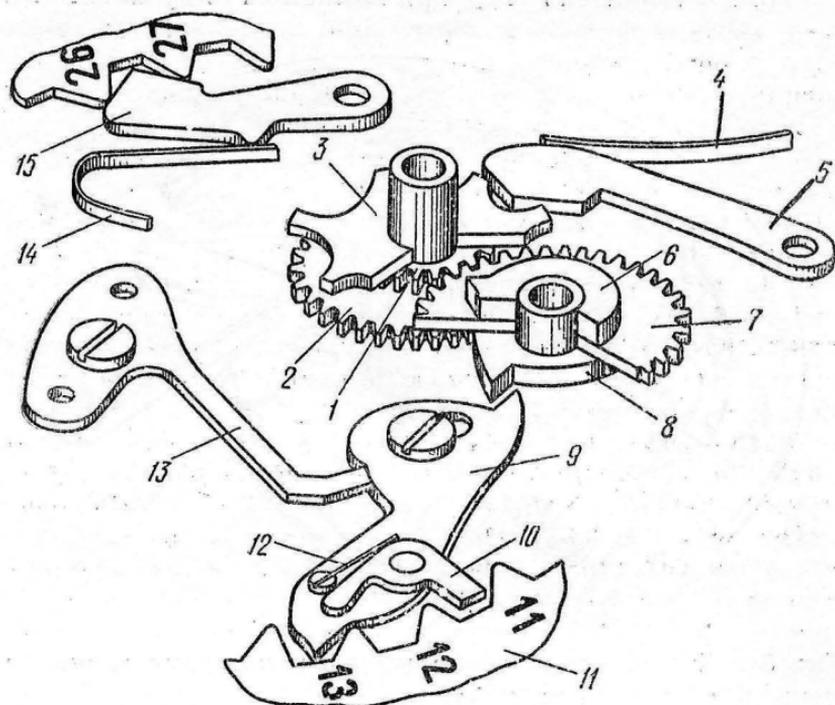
Кинематическая схема двойного календарного устройства часов 2428 «Слава»:
